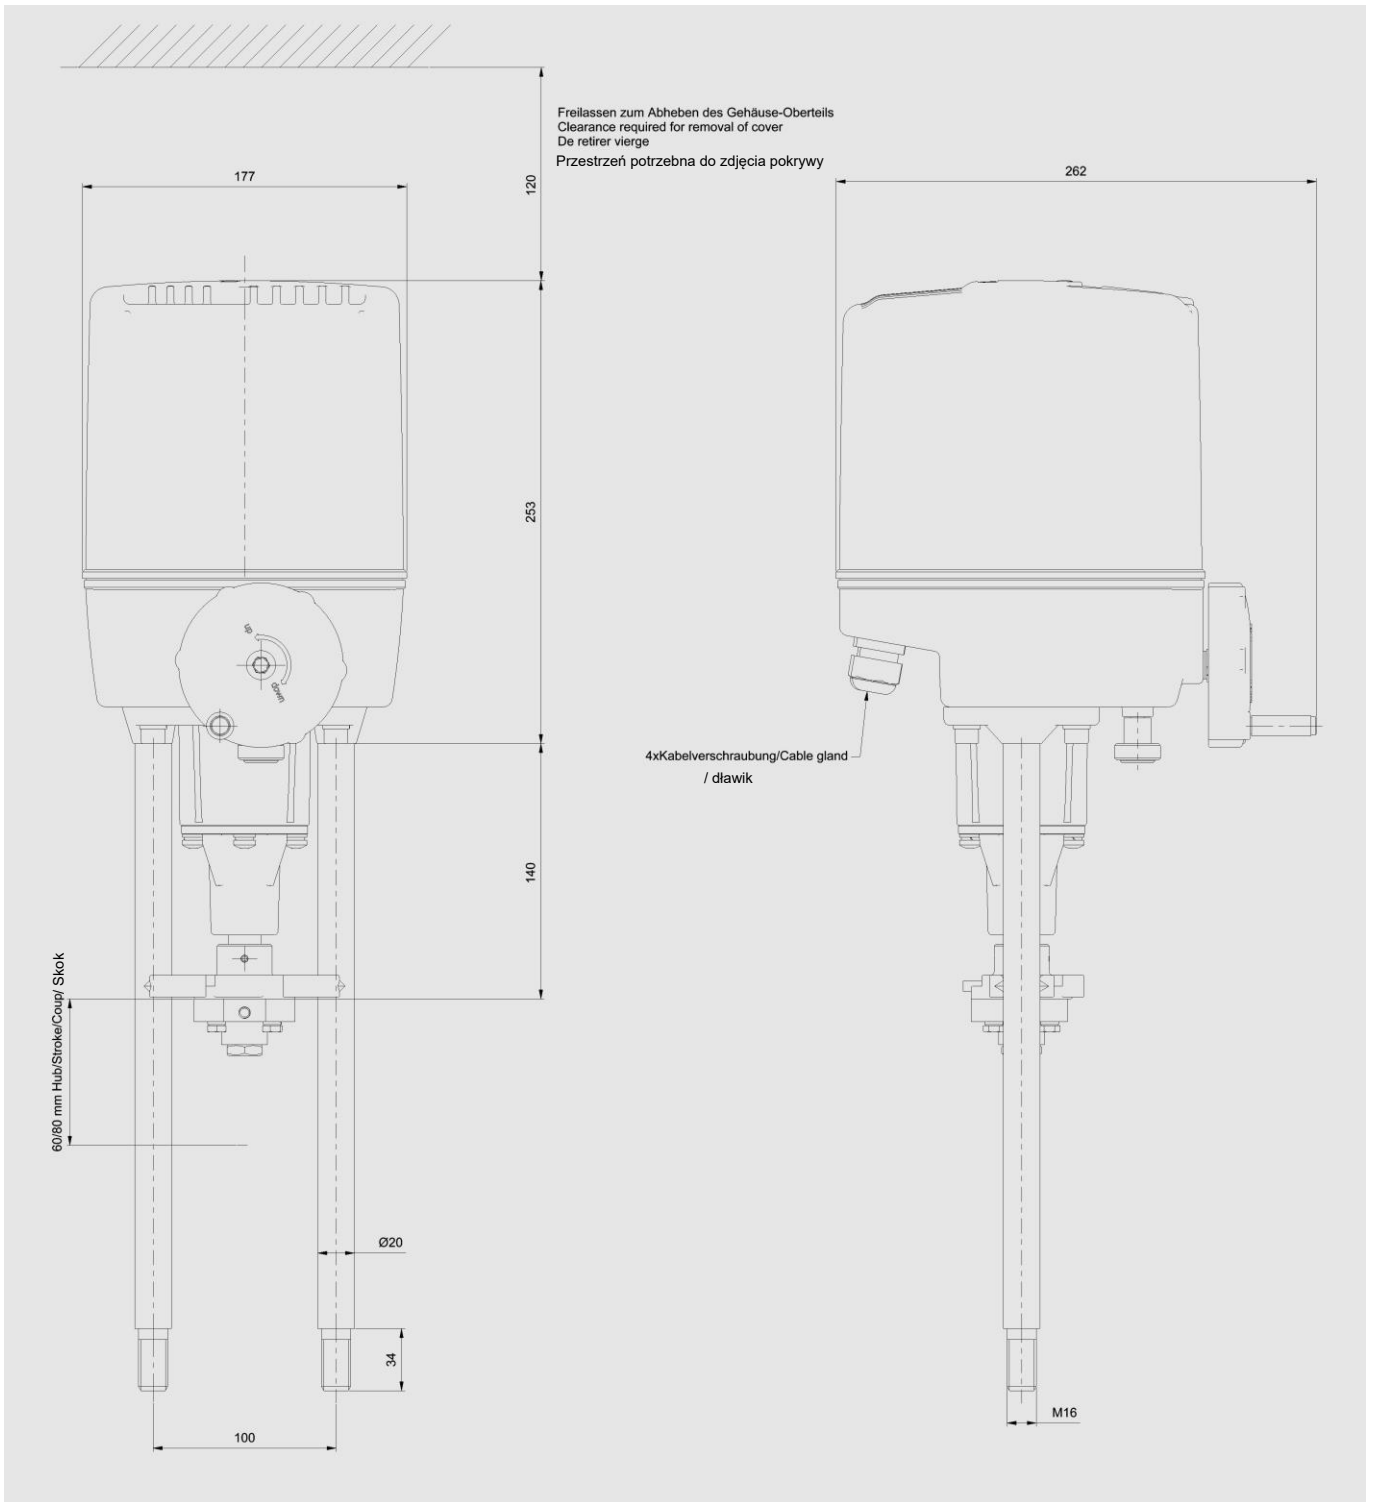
Maßblatt/Dimension sheet/ Wymiary
